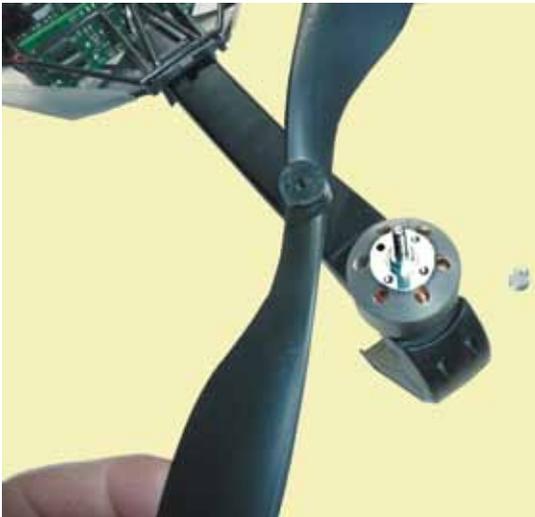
Die Motoren der beiden seitlichen Ausleger drehen sich gegen den Uhrzeigersinn. Auf sie sind mit „Left“ beschriftete Rotorblätter zu montieren.
